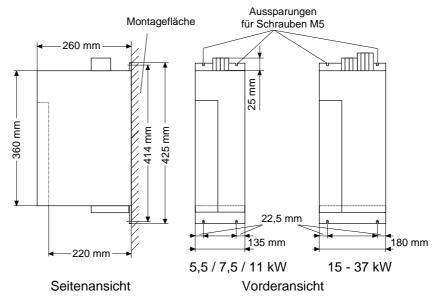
Maßbilder für Gehäusebreite 135 mm und 180 mm
